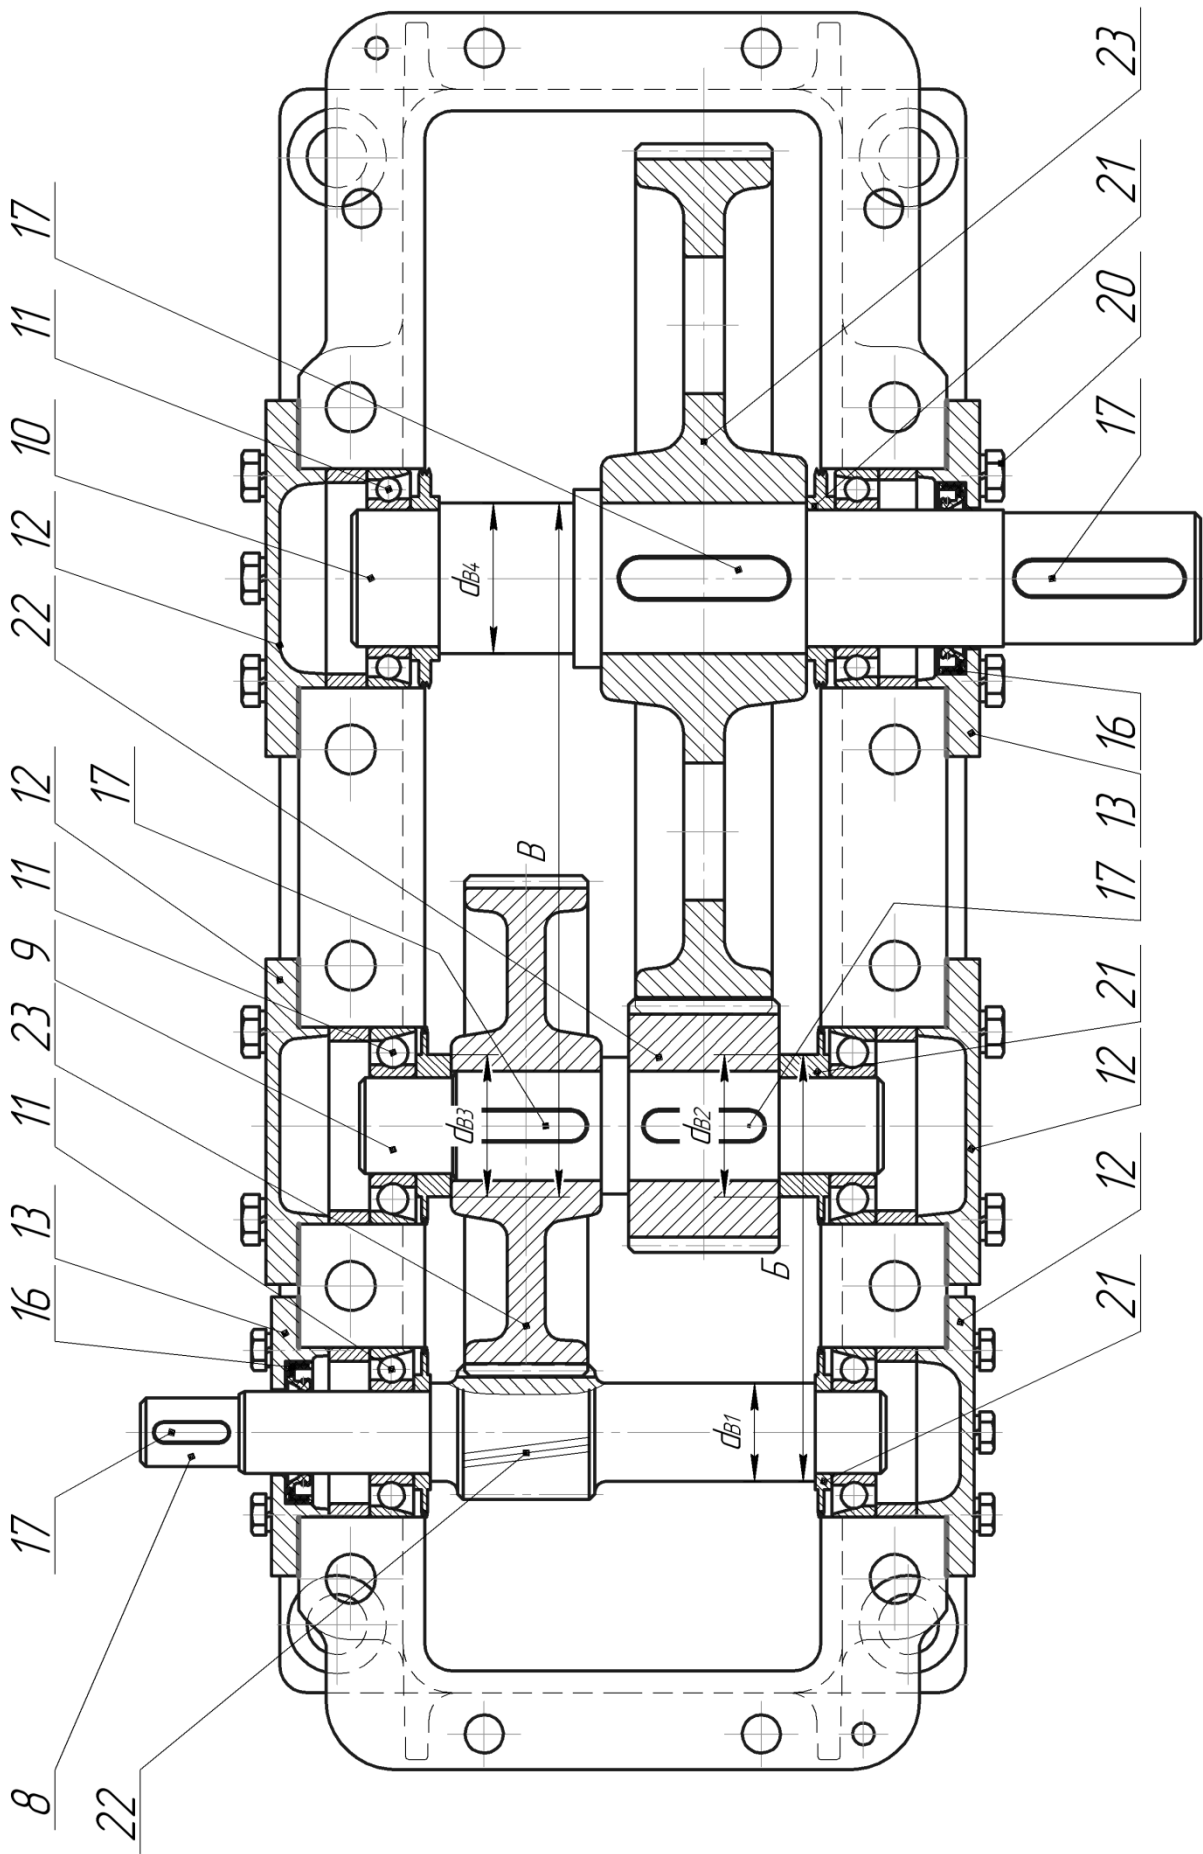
Конструкция двухступенчатого цилиндрического редуктора (вид сверху)
